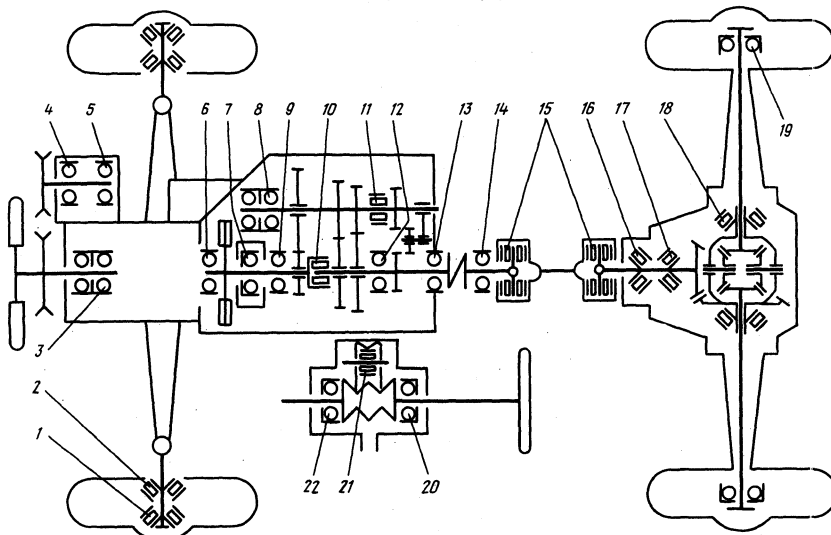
Схема расположения подшипников качения на автомобиле «Жигули»:
